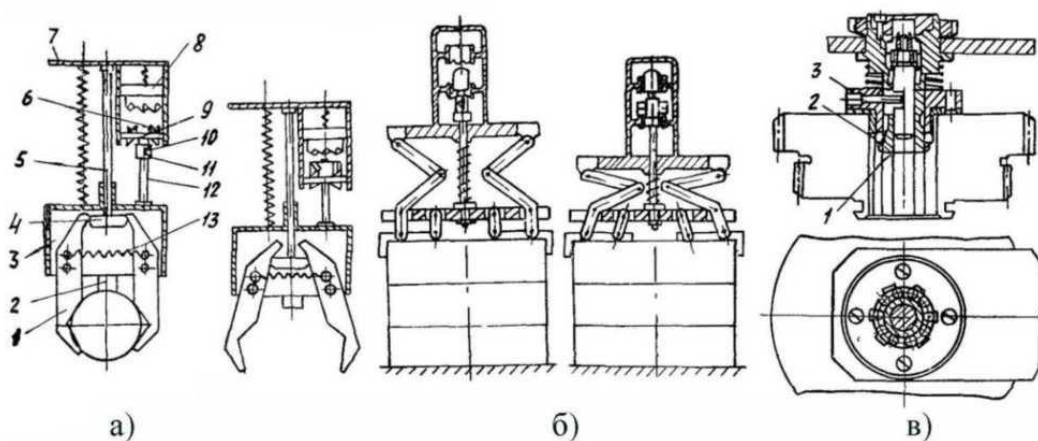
Схеми пристроїв для захоплення валів або фланців за зовнішню поверхню
